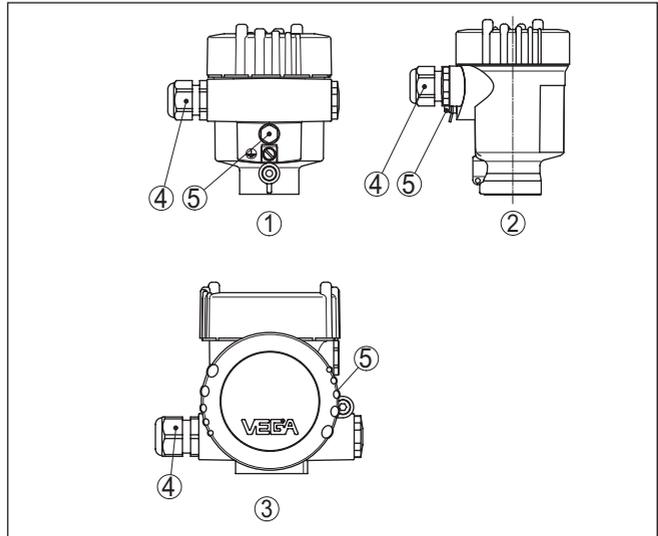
Posición del racor atornillado para cables y del elemento de filtro para diferentes versiones de carcasa
